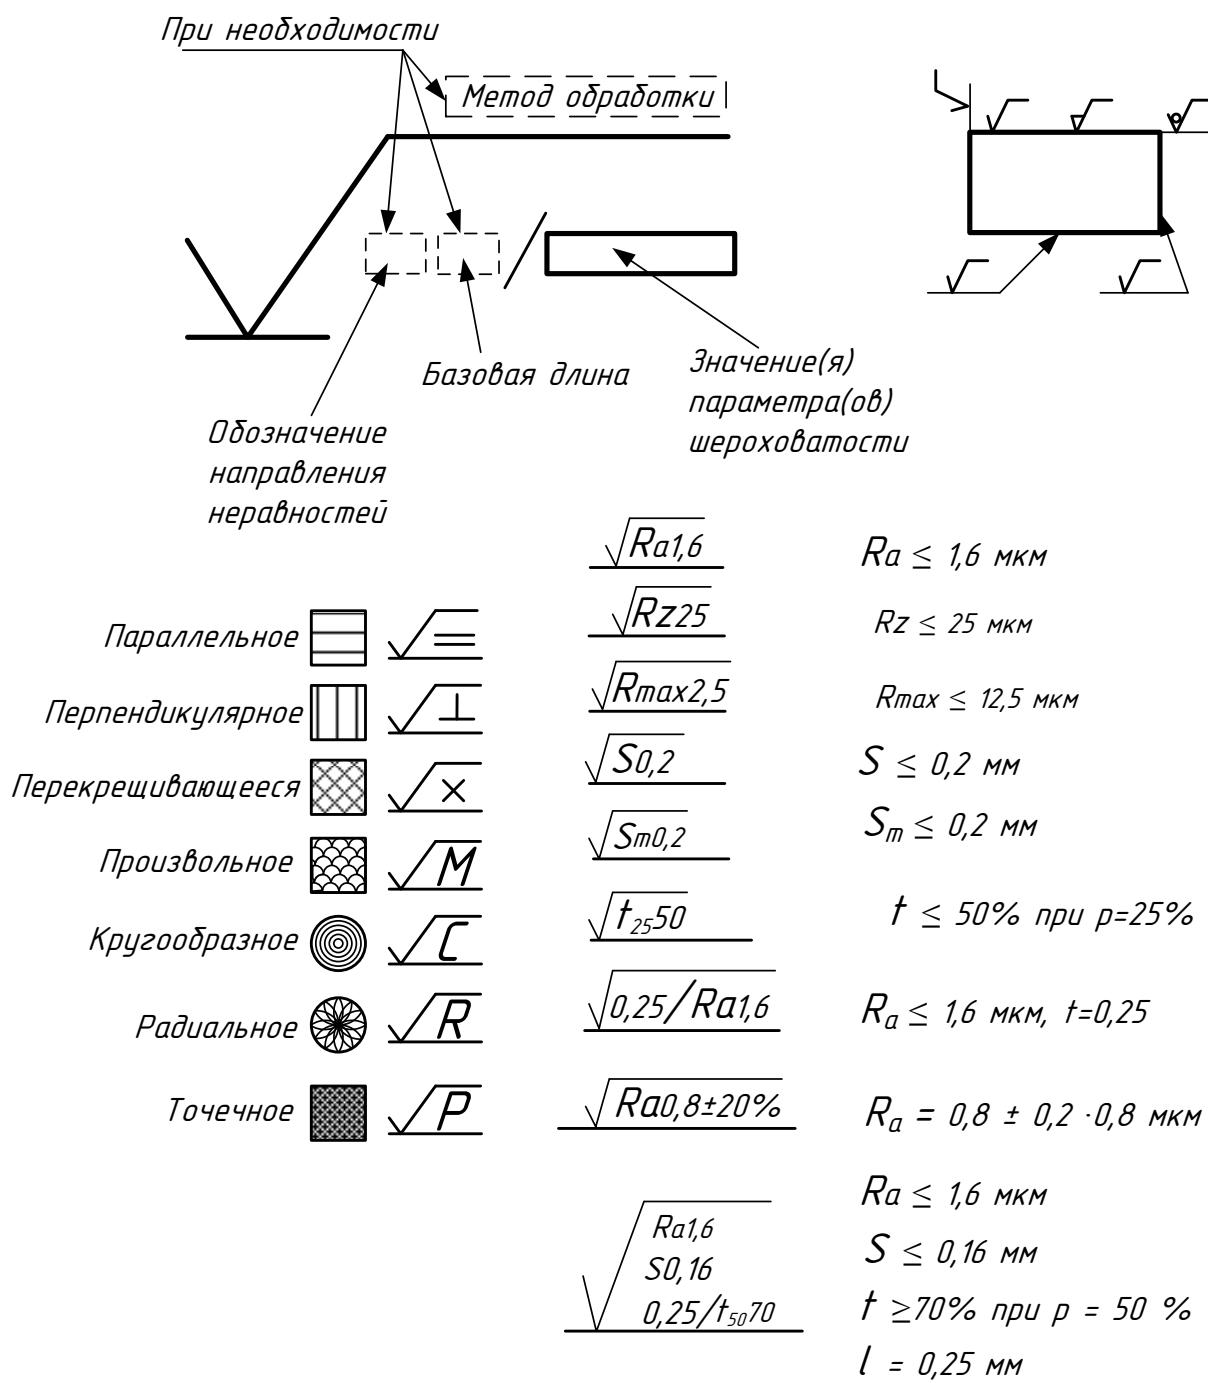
Структура и примеры обозначения шероховатости
